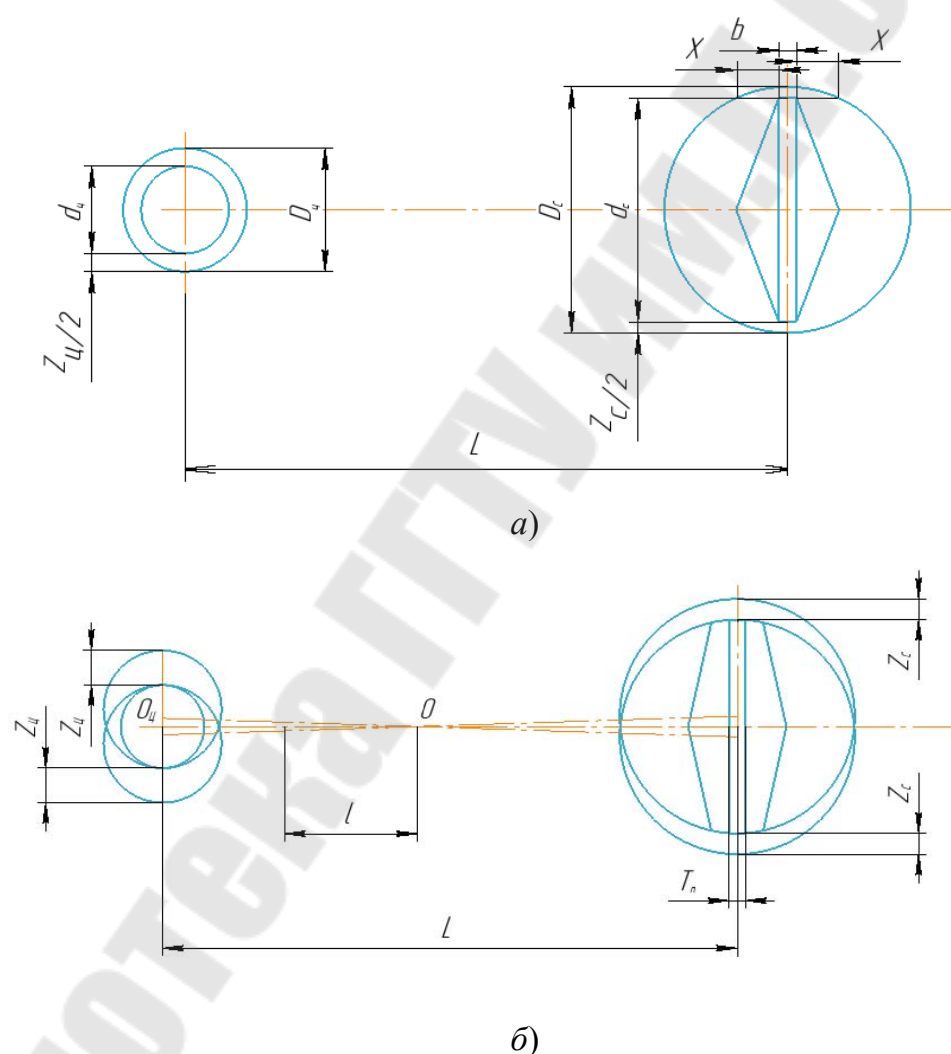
Схема установки заготовки на плоскость и два пальца:
